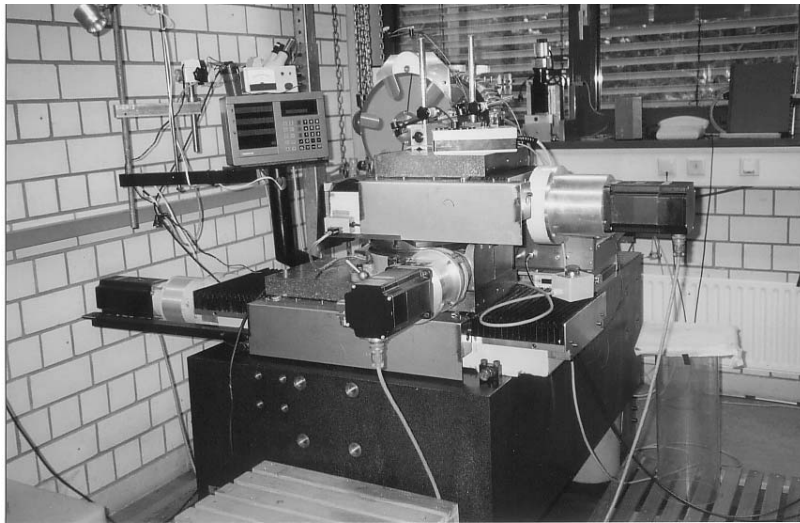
Die Ultrapräzisionsdrehmaschine des Lehrstuhls für Feinwerktechnik
